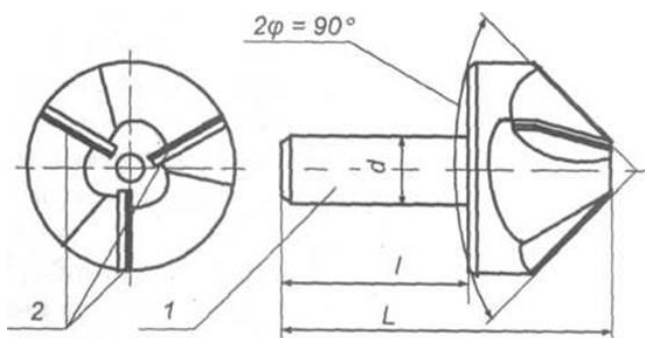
конструкція конічної зенківки, оснащеної пластинами з АТП: 1 – корпус зенківки; 2 – різальні пластини з АТП.
